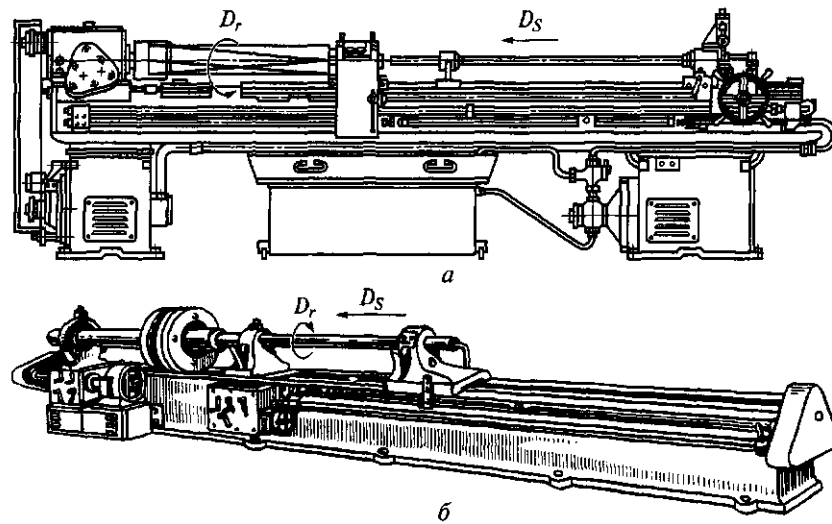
Горизонтально-сверлильные станки для глубокого сверления вращающихся (*a*) и неподвижных (*б*) заготовок:
